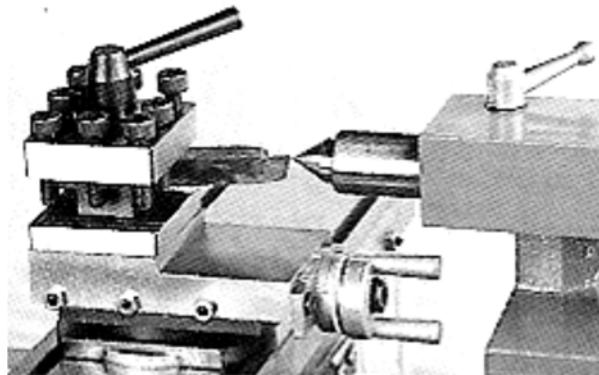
Einrichten der Bearbeitungswerkzeuge
